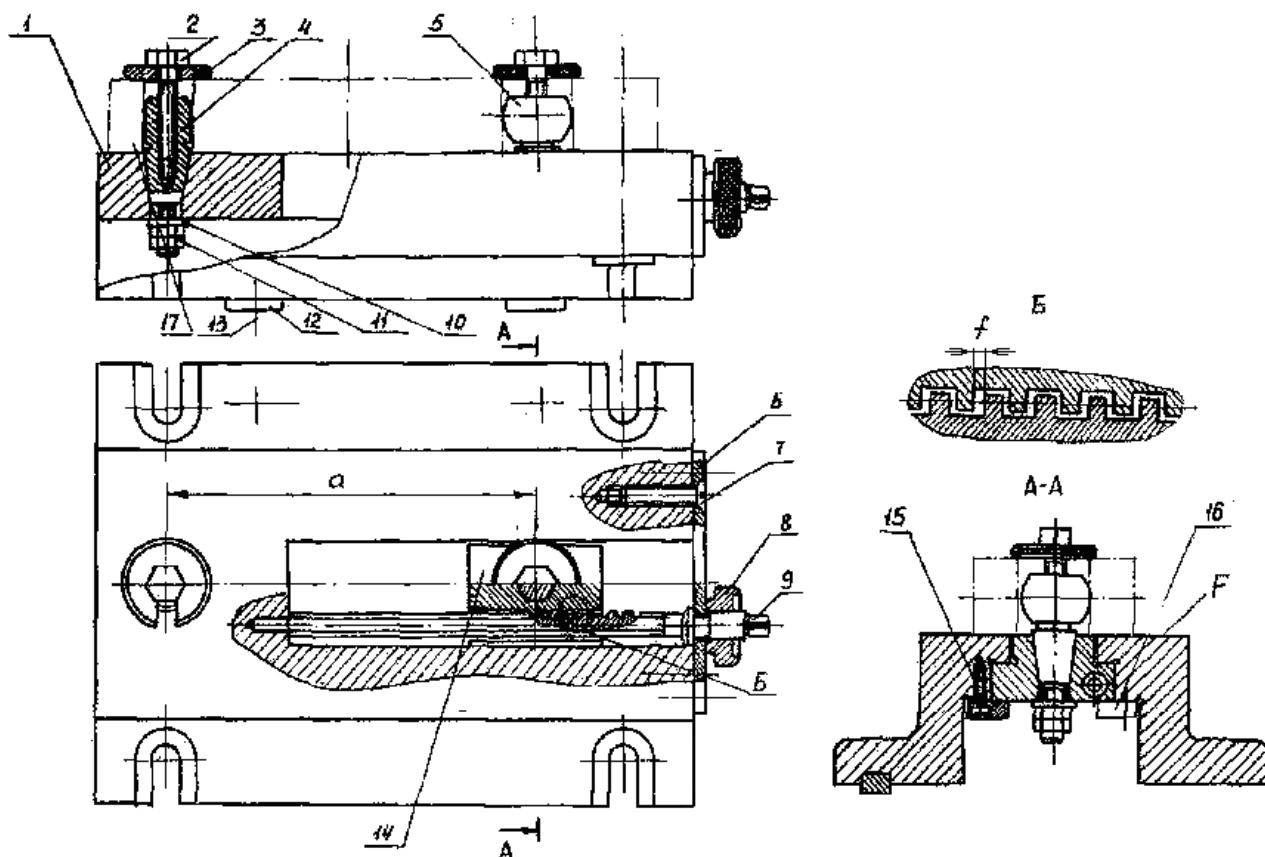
Приспособление для обработки заготовки по контуру
